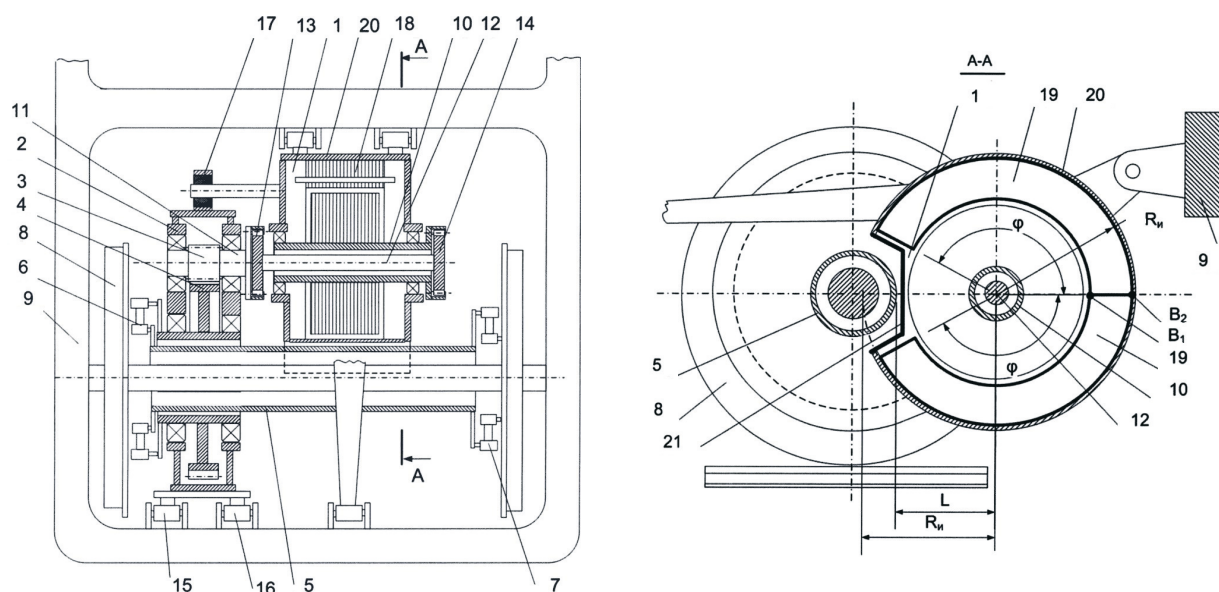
Тяговый привод с дугостаторным асинхронным ТЭД: 1 – ТЭД; 2 – редуктор; 3, 4 – зубчатые колеса; 5 – полый вал; 6, 7 – муфты; 8 – колесная пара; 9 – рама тележки; 10 – вал ТЭД; 11 – вал редуктора; 12 – торсионный вал; 13, 14 – зубчатые муфты; 15, 16 – опоры редуктора; 17 – подвижное соединение; 18 – статор ТЭД; 19 – дугообразные индукторы; 20 – корпус ТЭД; 21 – кожух
